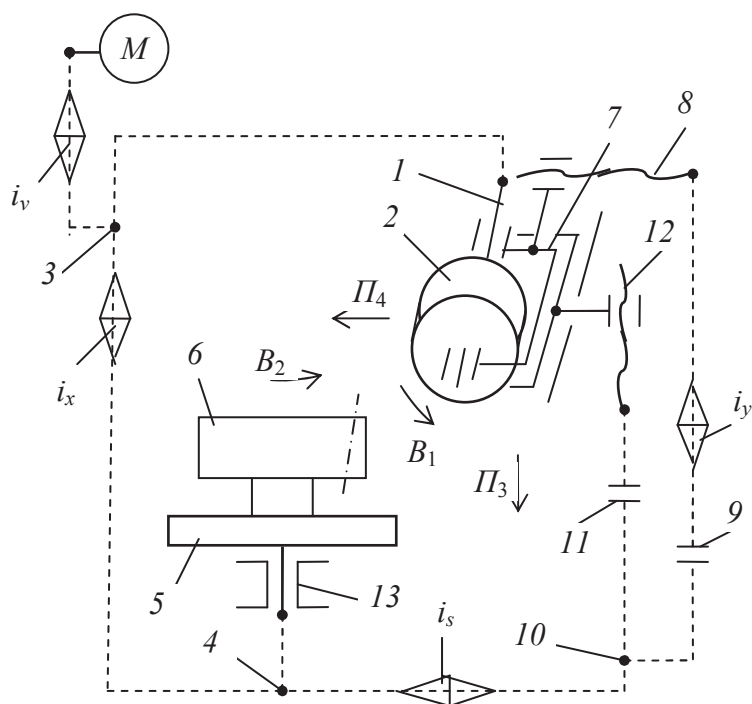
Структурная схема зубофрезерного станка для обработки колес с наклонными зубьями
